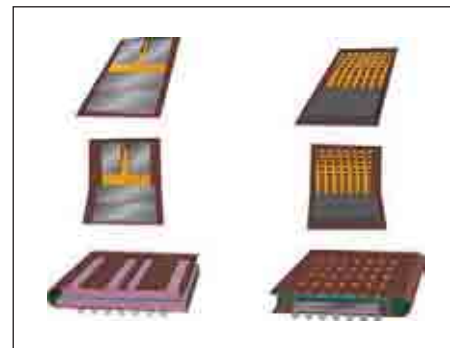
Пошаговая схема сборки пакета кристаллов микросхем
